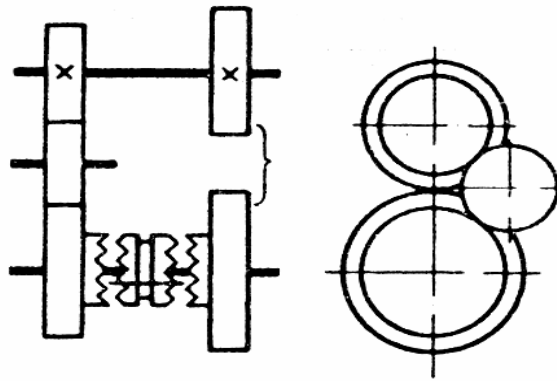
Реверсивный механизм с цилиндрическими колесами
